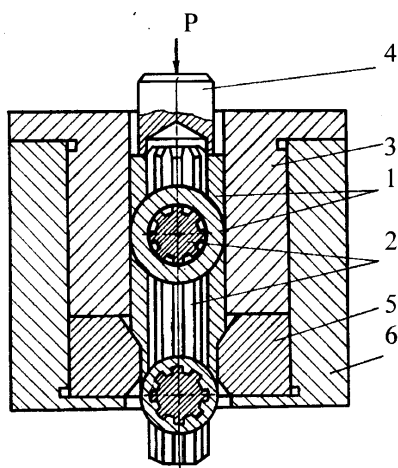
Схема процесса формообразования внутренних шлицев в трубных заготовках
